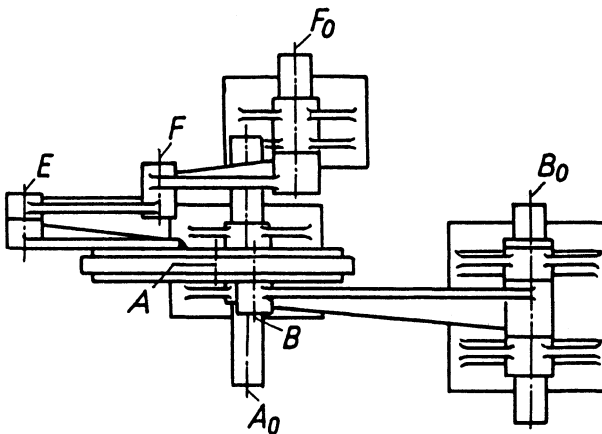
Grundriß des Getriebes nach Bild 4.27
